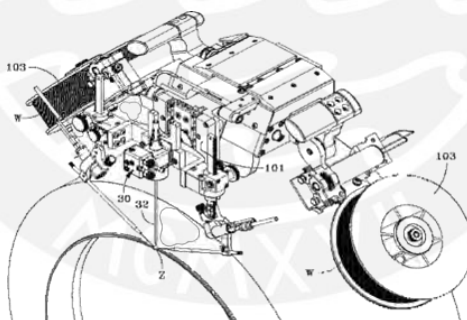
4 Lincoln Global sistema automatizado de soldadura orbital
